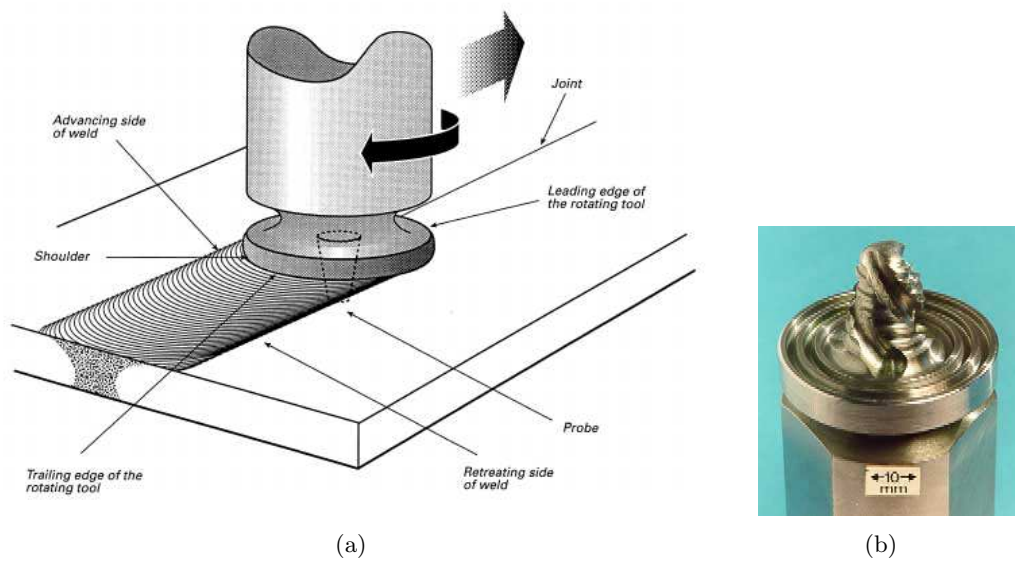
(a) Schéma du procédé de soudage par friction-malaxage [Thomas et Nicholas, 1997]. (b) Outil de soudage (TWI).
